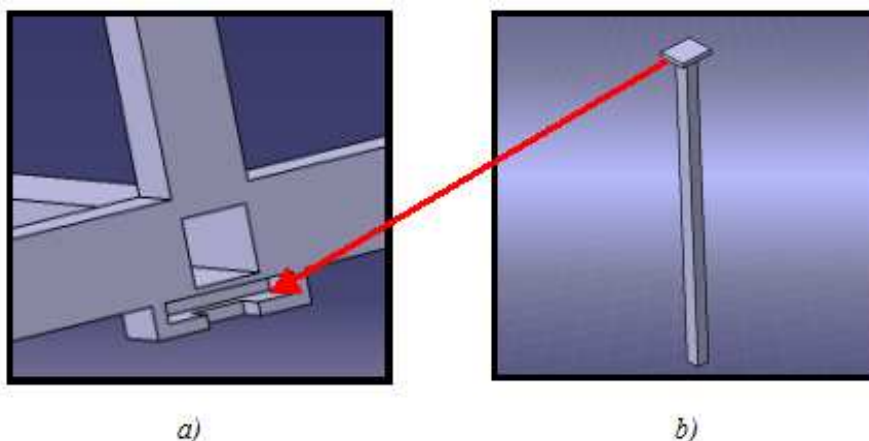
15: Soportes al firme. a) Detalle soporte estructura móvil. b) Detalle apoyo.
